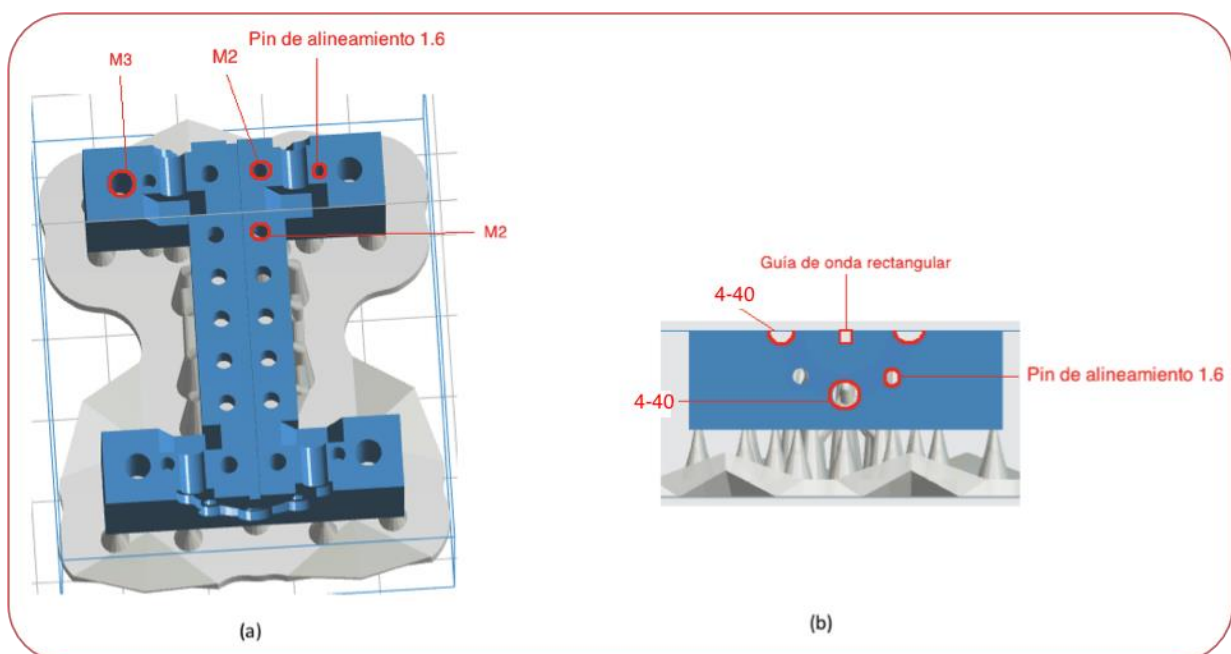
(a) Esquema de métrica de tornillo para ensamblaje en el interior de la guía; (b) Esquema de métrica de tornillo para ensamblaje en el flange de la guía.
